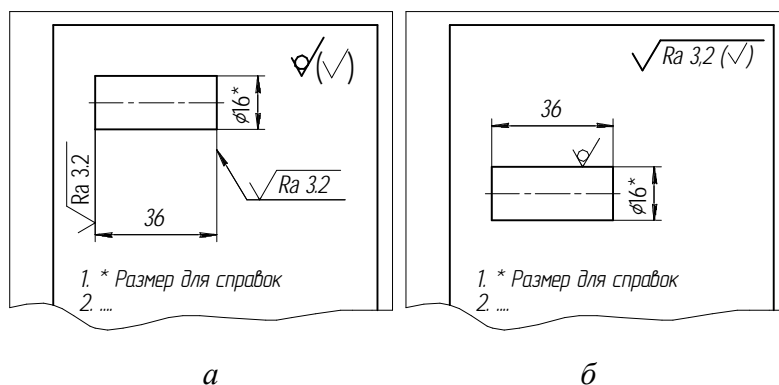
Чертеж детали с поверхностью Ø16, которая по данному чертежу не обрабатывается
